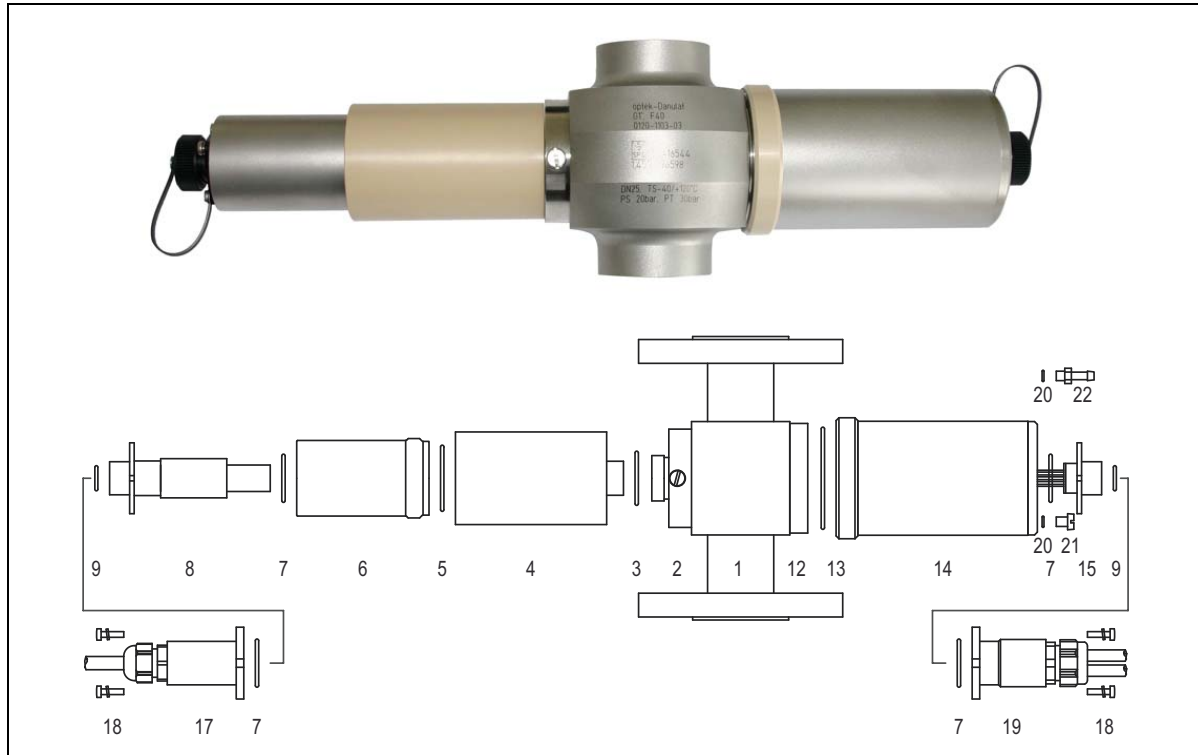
Foto y dibujo de despiece del TF56-HT-N
